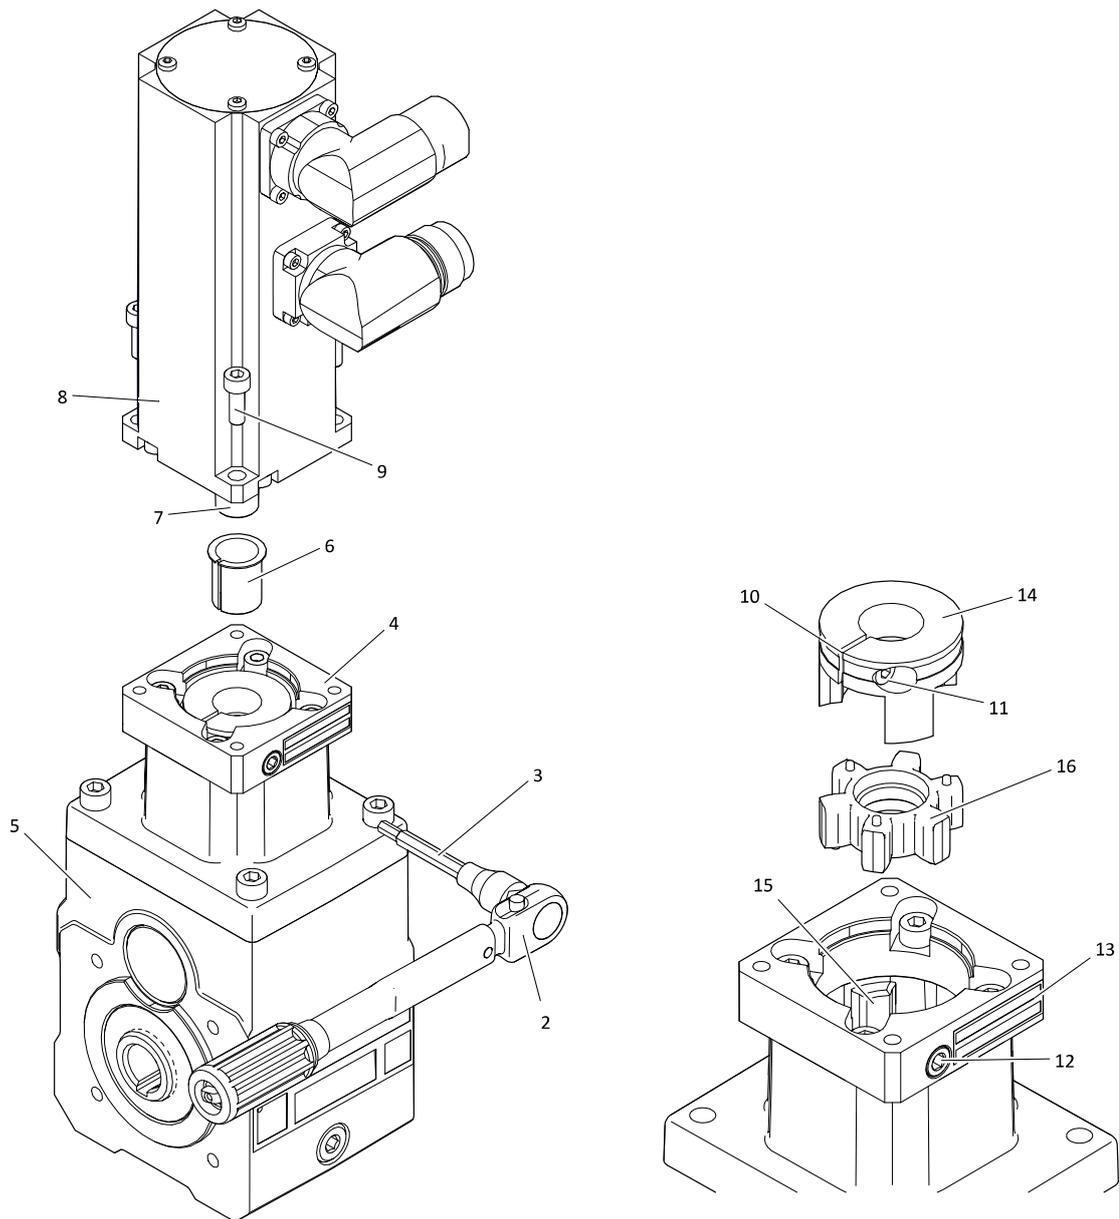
Montage eines Motors an ein Kegelradgetriebe KL mit Motoradapter MQ (Beispiel)
